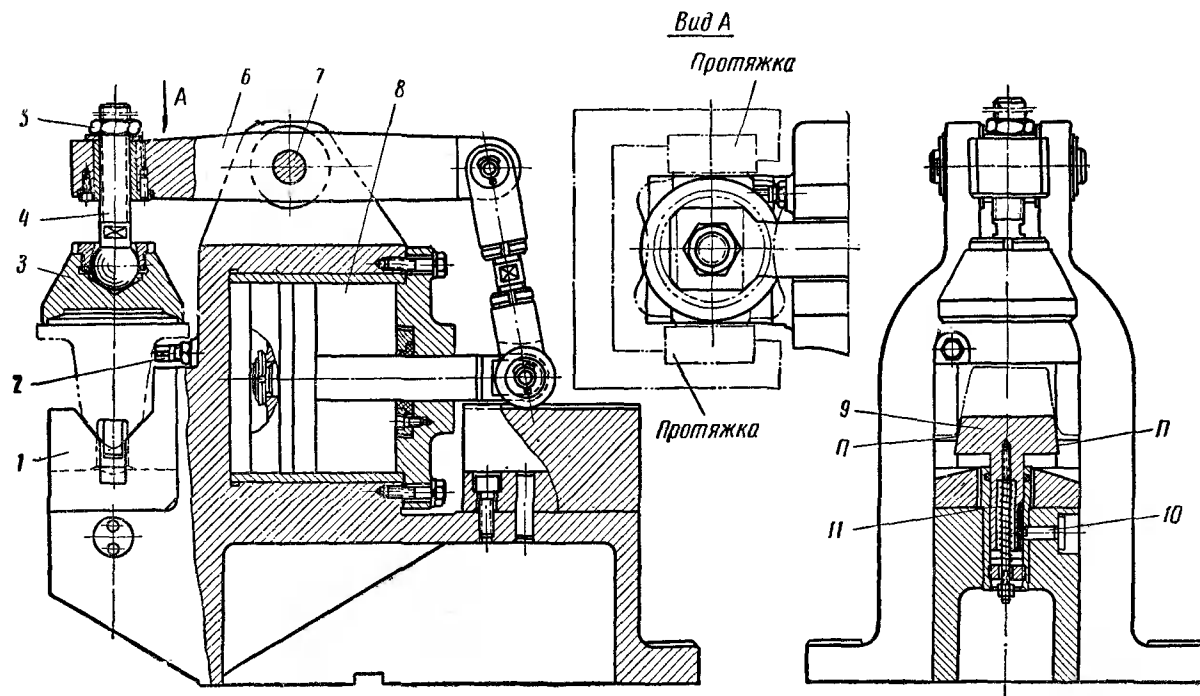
Приспособление для обработки плоскостей ушков вилки кардана
